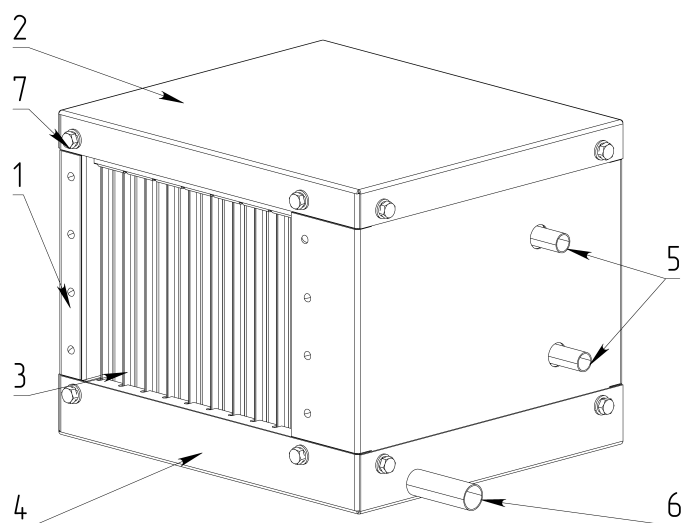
Внешний вид воздухоохладителя стандартного исполнения (левая сторона обслуживания)
